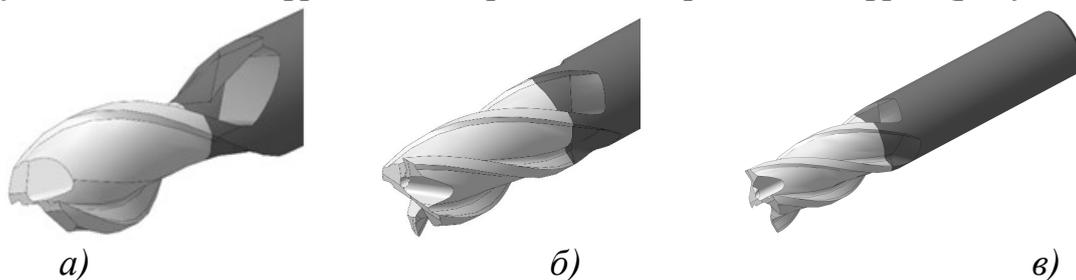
3D–модели фрез: с двумя режущими зубьями (а); с увеличенным диаметром (б); с углом винтовой канавки равной  $38^\circ$
